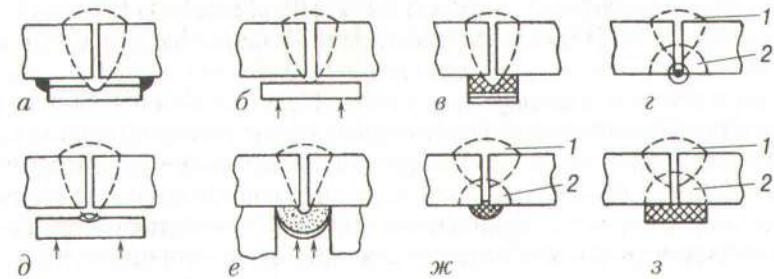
Схеми пристроїв для утримання зварювальної ванни та шлаку й формування зворотного валика при зварюванні під флюсом:
